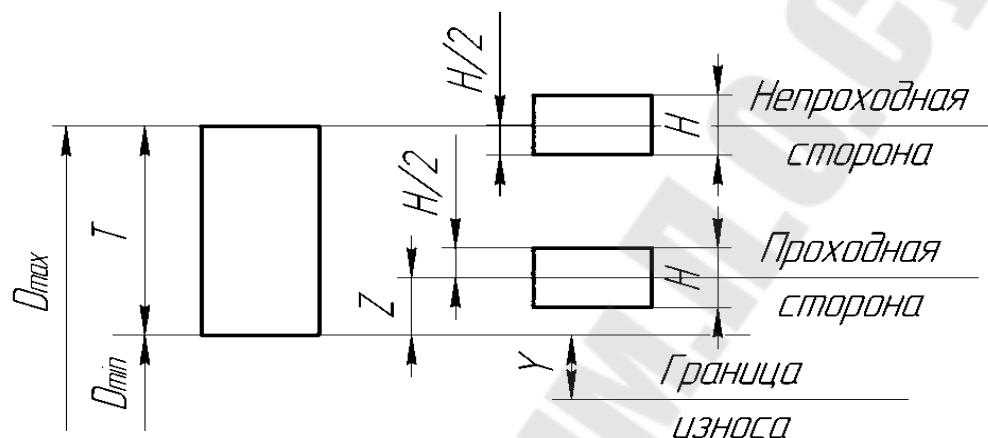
Схема расположение полей допусков калибров-пробок
